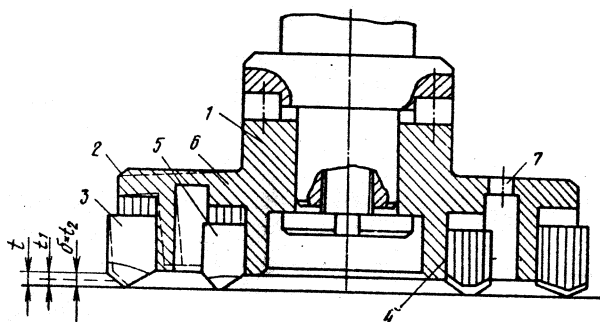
Торцева фреза по а. с. 623311 МКИ В 23 С 5/06
